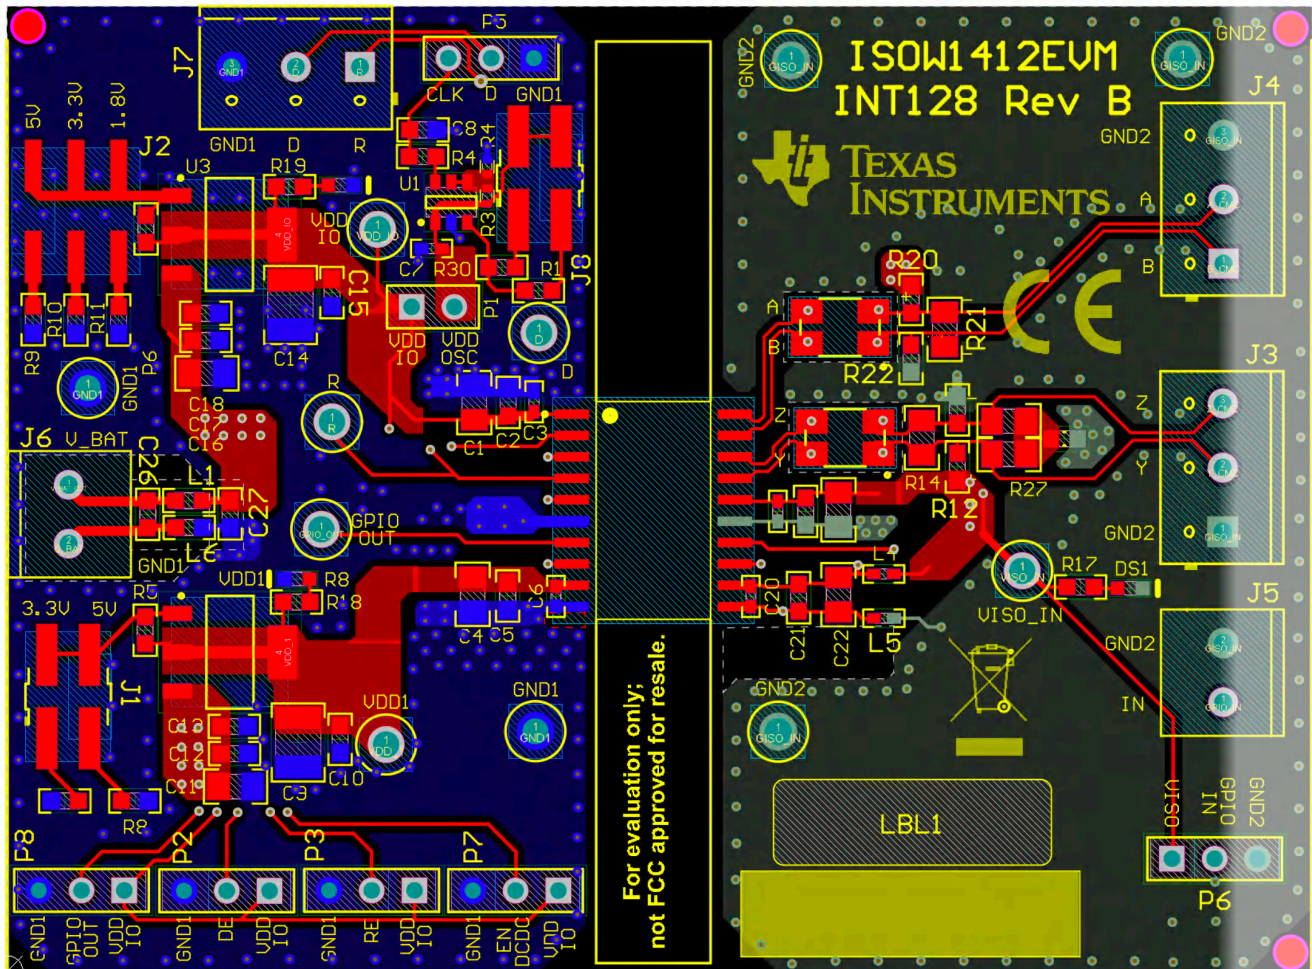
ISOW1412DFMEVM PCB 布局 - 顶层
